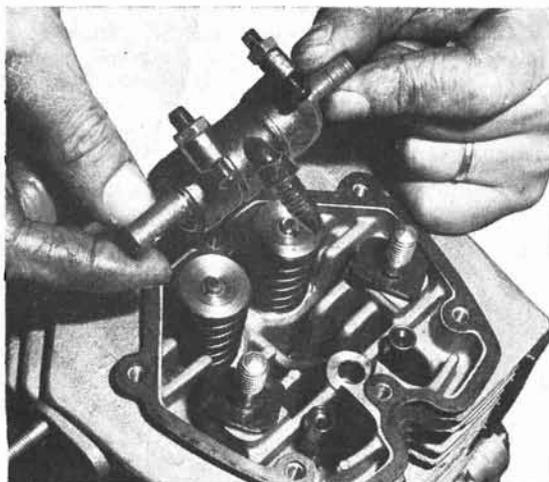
Repose d'une rampe de culbuteurs (Photo RMT)
